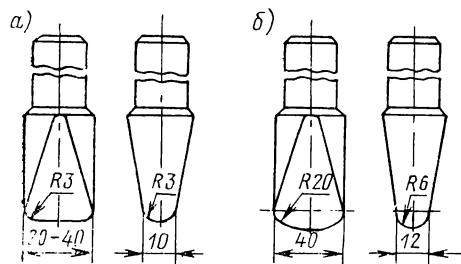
Рабочая часть зубила для проколачивания сварных швов стыковых (а) и тавровых (б) соединений.
